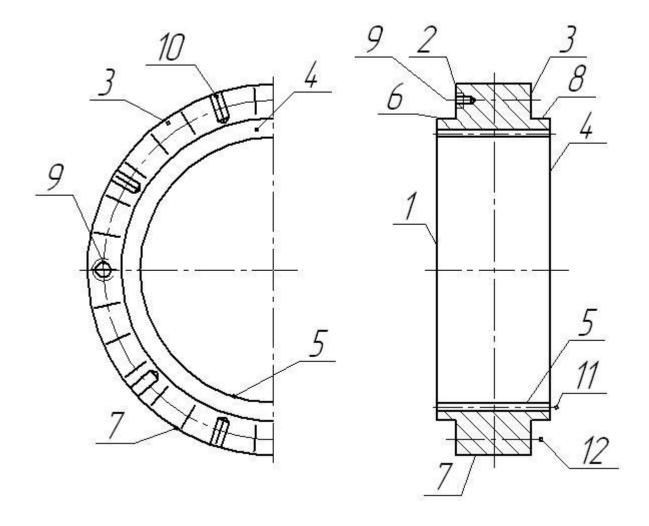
Эскиз шестерни - зубчатого колеса с внутренним зацеплением.
